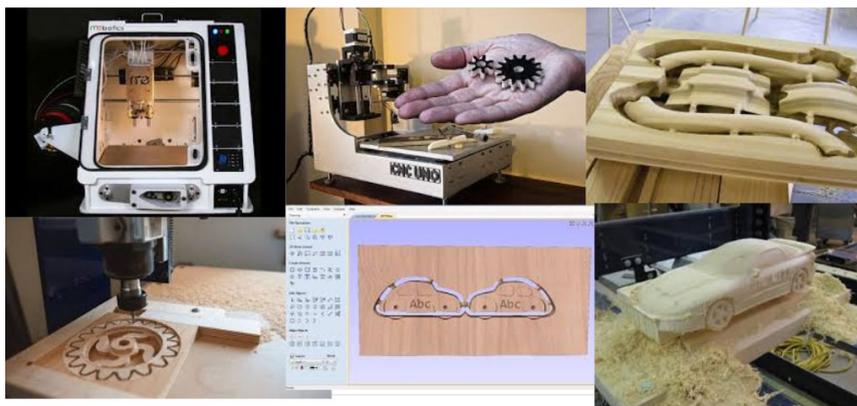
Exemplos de objetos produzidos por uma fresadora cnc
